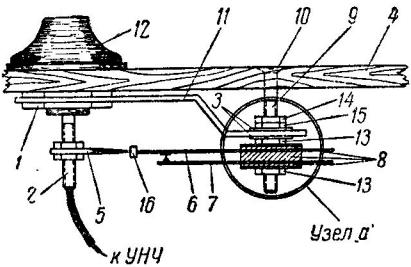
Сборочный чертеж. 1. Гайка крепления изогнутой пластины. 2. Удлиненная ось звукоснимателя. 3. Шайбы. 4. Панель проигрывателя. 5. Рычаг. 6—7. Контакты включателя. 8. Изоляционные прокладки. 9. Регулировочный винт. 10. Головка регулировочного винта. 11. Изогнутая пластина крепления узла «а». 12. Кронштейн звукоснимателя. 13. Гайки крепления блока контактов. 15 и 14. Гайка и контргайка, крепящие изогнутую пластинку к регулировочному винту. 16. Т-образный конец контакта.
